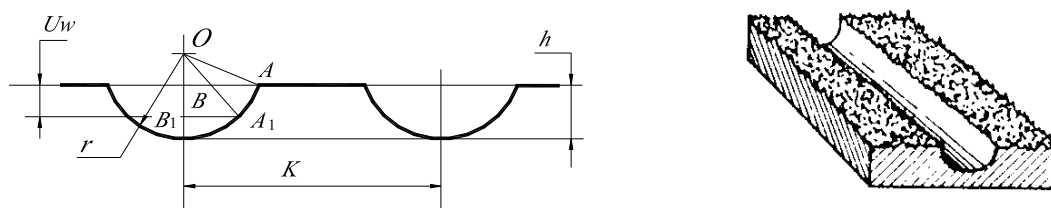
Розрахункова схема і вигляд канавок круглої форми
